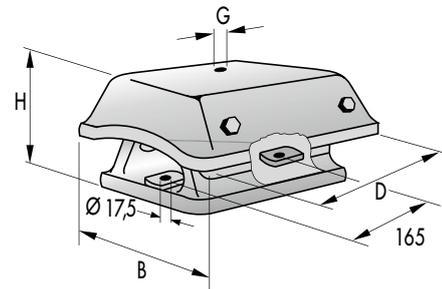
Maschinenlager 050 18 002, 050 18 004
